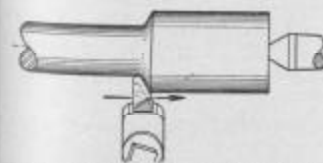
Emplai de l'outil à tourner à coupe de la gauche
